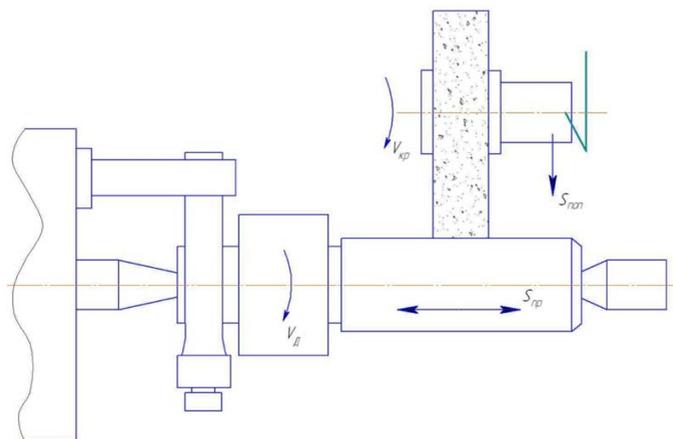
Схема круглого шлифования цилиндрической поверхности
